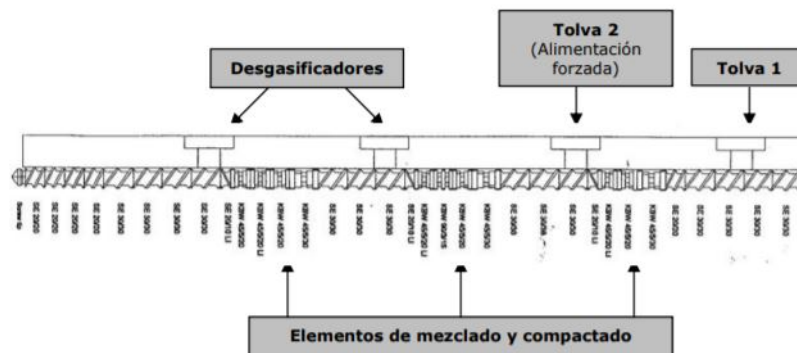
Diseño de los tornillos engranados de la extrusora Brabender DSE 20
